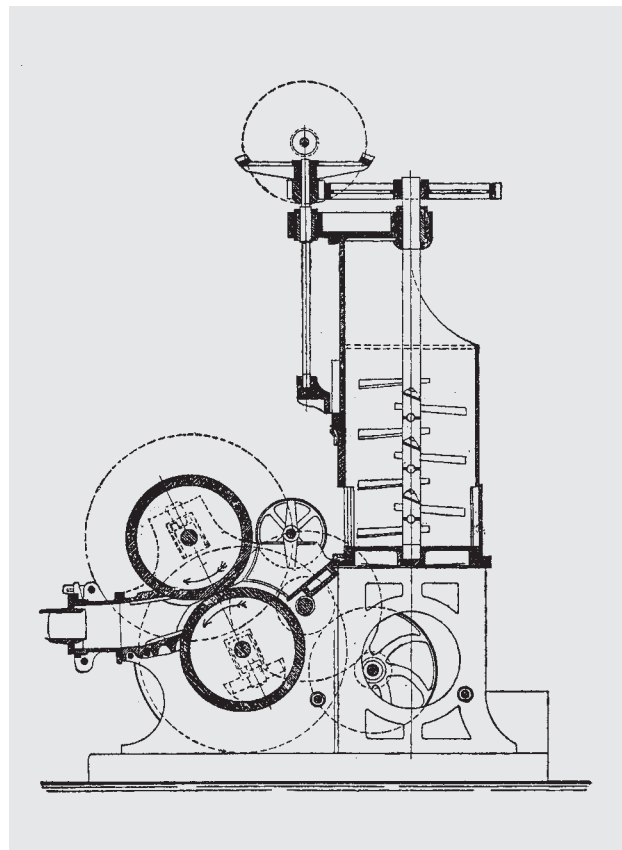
Walzenpresse mit Tonzuführung über einen stehenden Tonschneider
